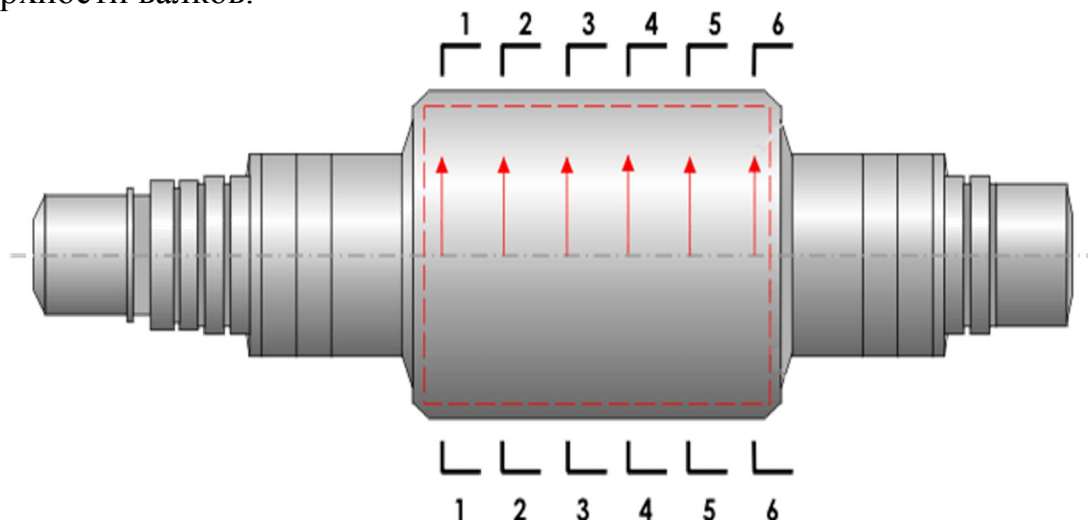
Схема контроля методом МПМ по рабочей поверхности валков: --- зона контроля рабочей поверхности вала; 1, 2, 3, 4, 5, 6 - номера сечений; -> - направление движения регистрирующего устройства прибора типа ИКН.
